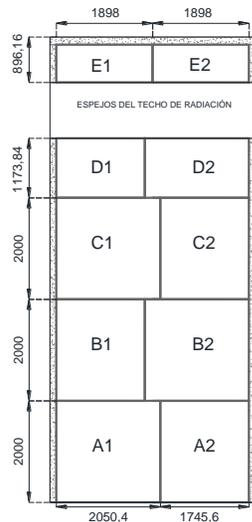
Distribución de juntas de expansión en paredes frontales. Fuente: Planos del proyecto
